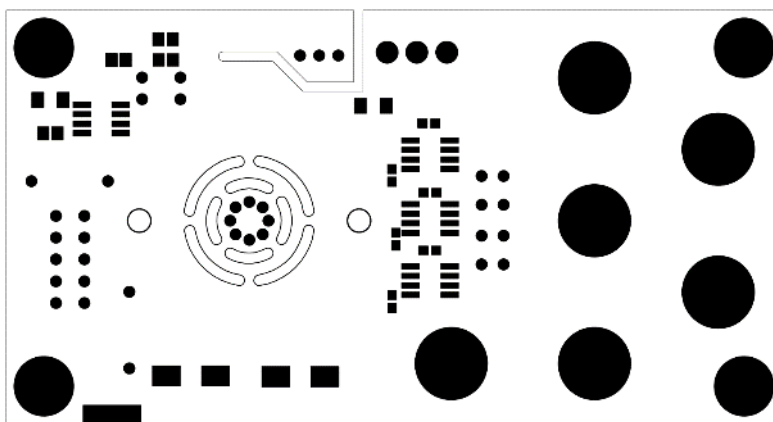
Vodivý motív prvej vnútornej vrstvy
